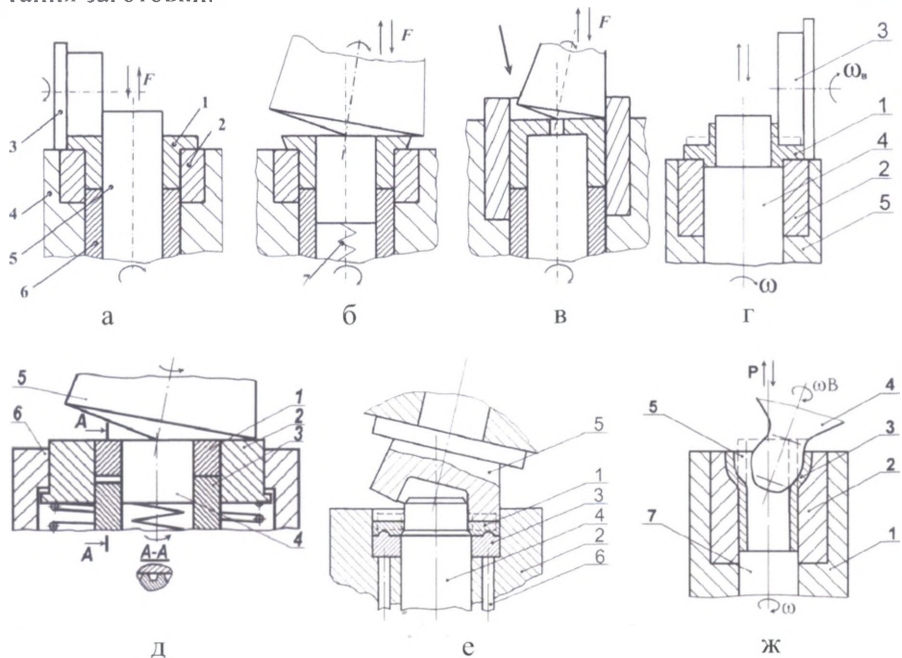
Схеми торцевого розкочування циліндричним і конічним валками: висаджування зовнішнього бурта (а), (б); висаджування внутрішнього бурта (в); висаджування і зворотнє витискування (г); пряме витискування зубчастої поверхні (д); осаджування-калібрування (е); роздавання-калібрування (ж)
